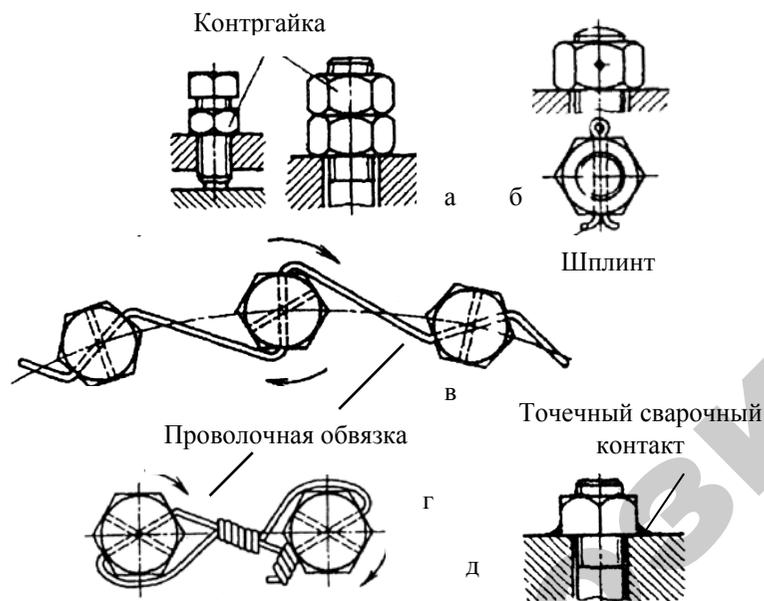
Способы стопорения крепежных резьбовых деталей
